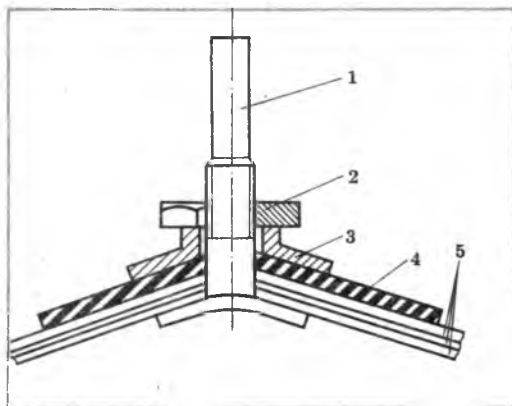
Приспособление для полировки стекол: 1 — металлический стержень (зажимается в дрель); 2 — гайка; 3 — профильная шайба; 4 — резиновый грибок; 5 — фетровые диски
